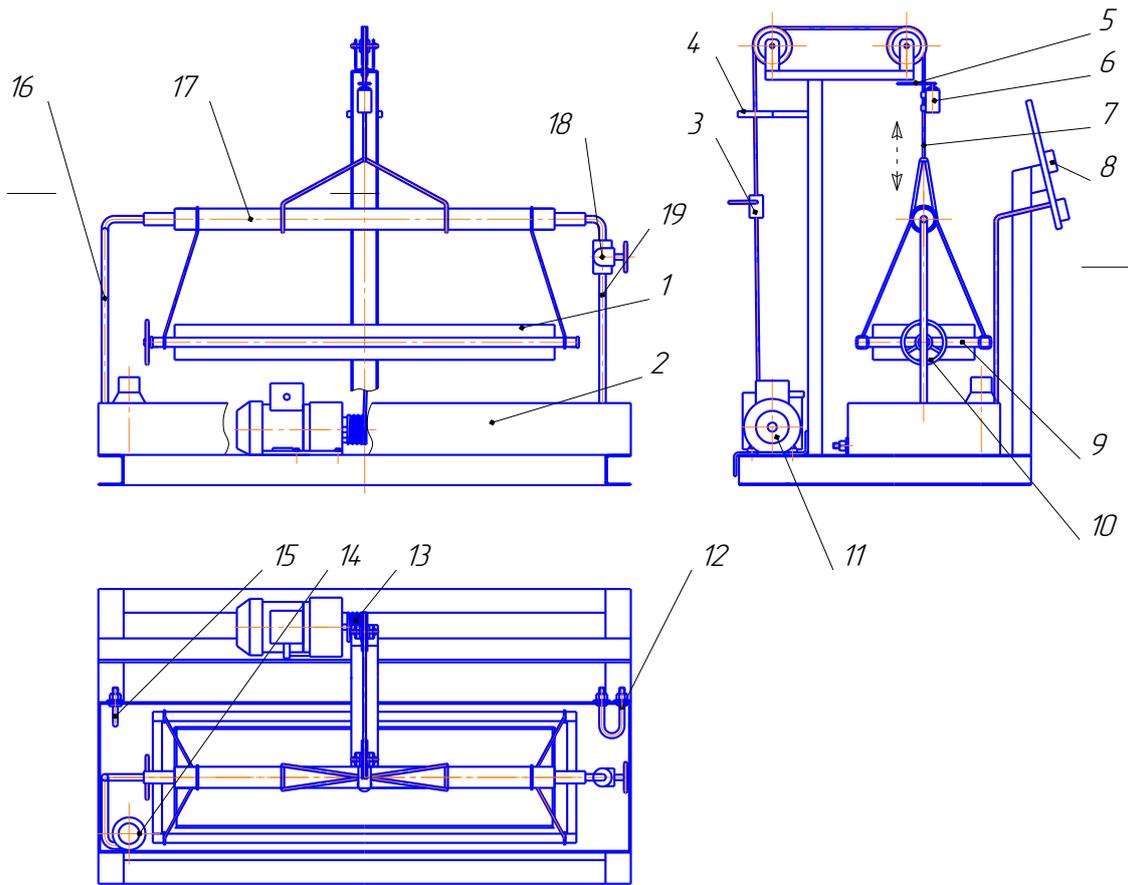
Установка для проращивания зерна: 1 – решето; 2 – ванна; 3 – выключатель концевой рычажковый; 4 – кольцо; 5 – лист; 6 – выключатель концевой кнопочный; 7 – трос; 8 – пульт управления; 9 – рама; 10 – вороток; 11 – мотор-редуктор; 12 – трубчатый электронагреватель; 13 – катушка; 14 – насос; 15 – датчик температуры; 16 – трубопровод нагнетательный; 17 – трубка для орошения; 18 – кран регулировочный; 19 – трубка сливная
